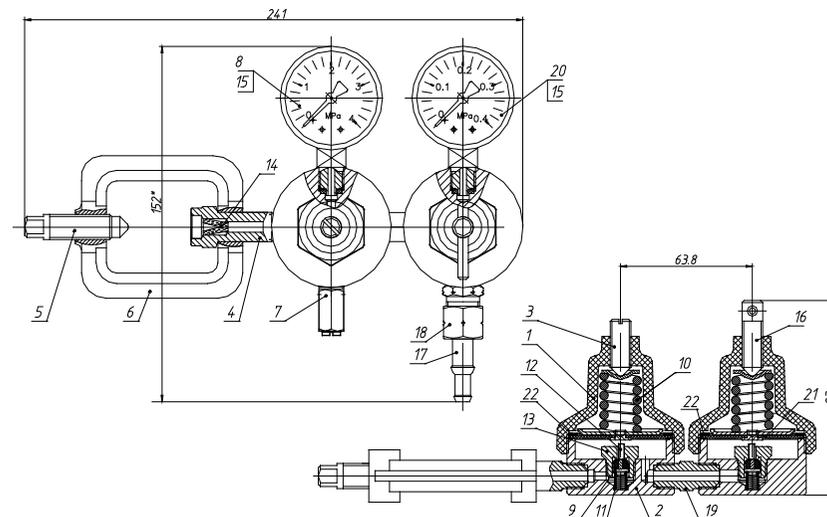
Редуктор баллонный ацетиленовый двухступенчатый:
